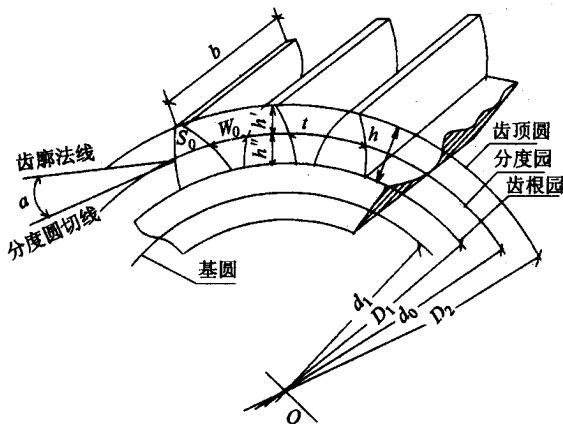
渐开线直齿圆柱齿轮各部分名称、符号
